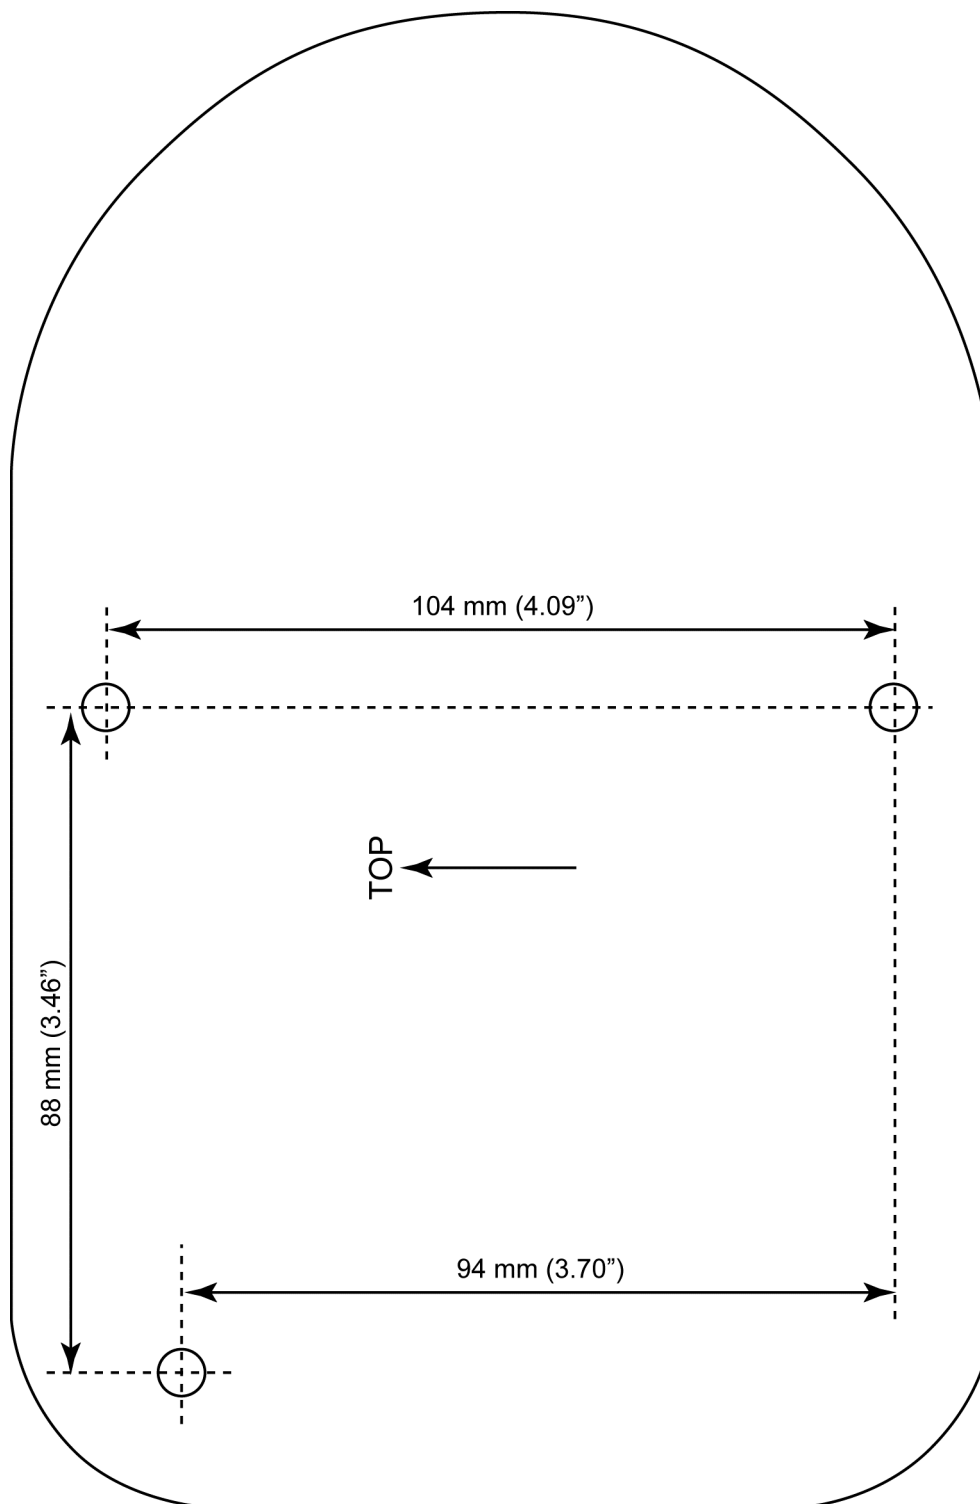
Шаблон для сверления заднего узла фотоприемника
